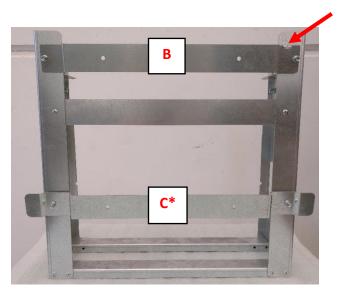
Installazione staffe sul box batterie: il verso di installazione
